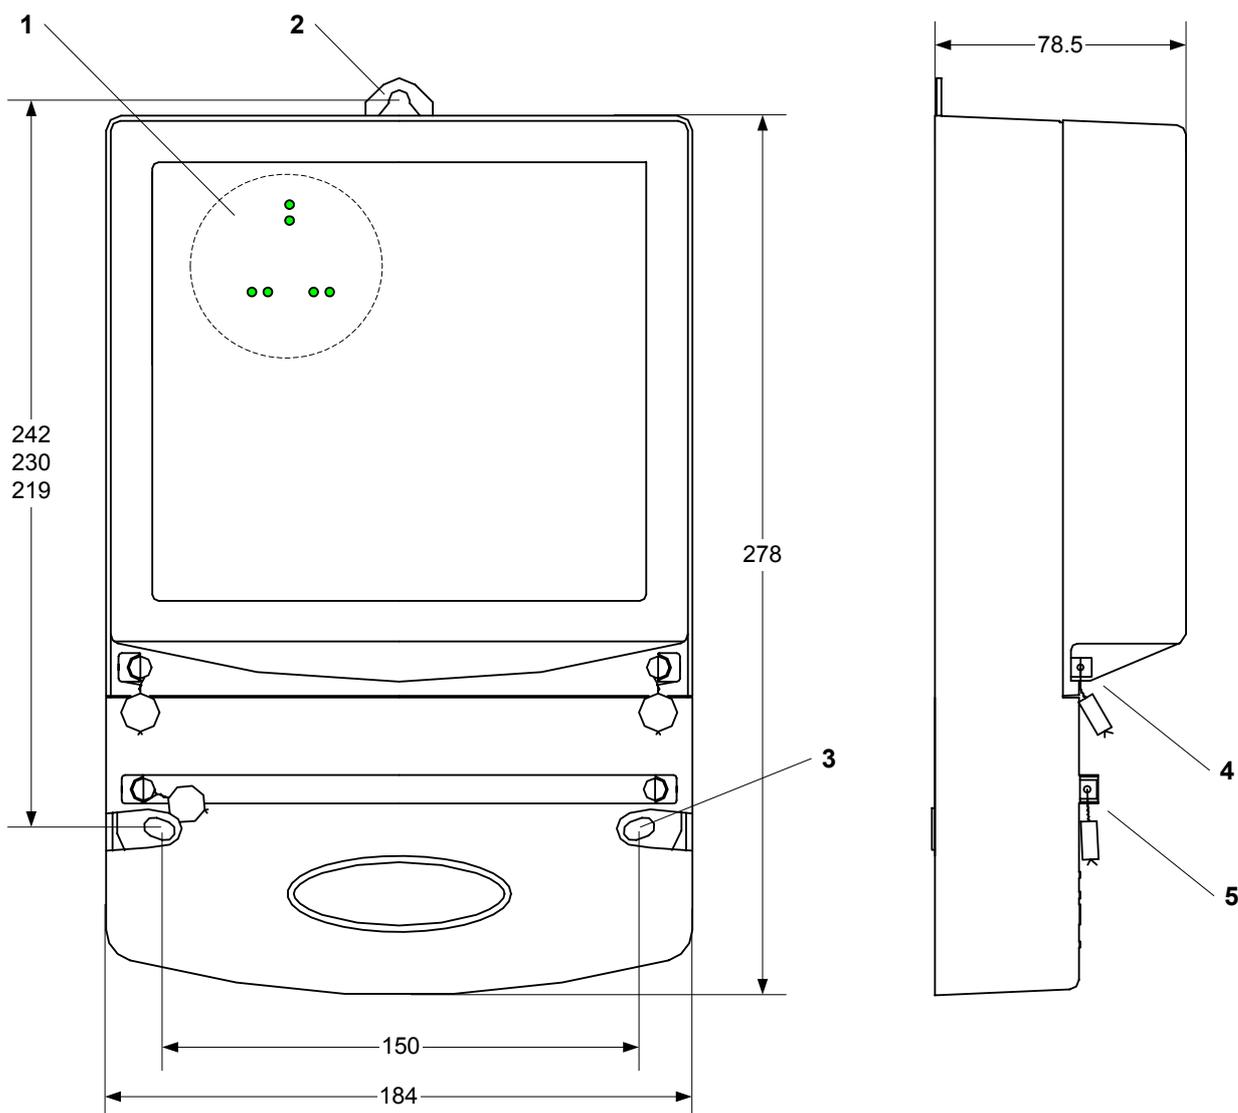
Внешний вид, габаритные и установочные размеры маршрутизатора
